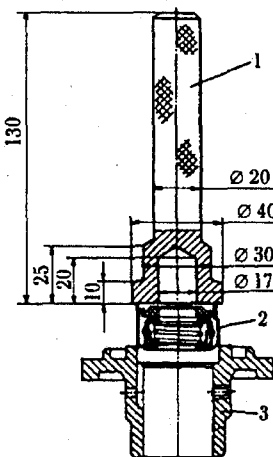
Запрессовка манжеты гидронасоса: 1 – оправка; 2 – манжета; 3 – корпус насоса
